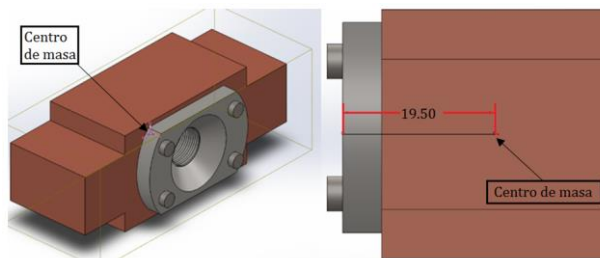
Masa excéntrica (conjunto masa de cobre - tuerca embalada).
